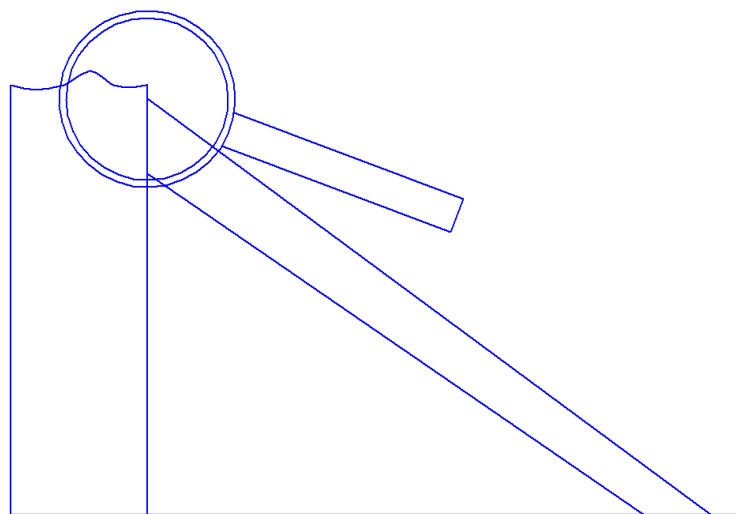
Контроль качества сварных швов конструкции стойки
